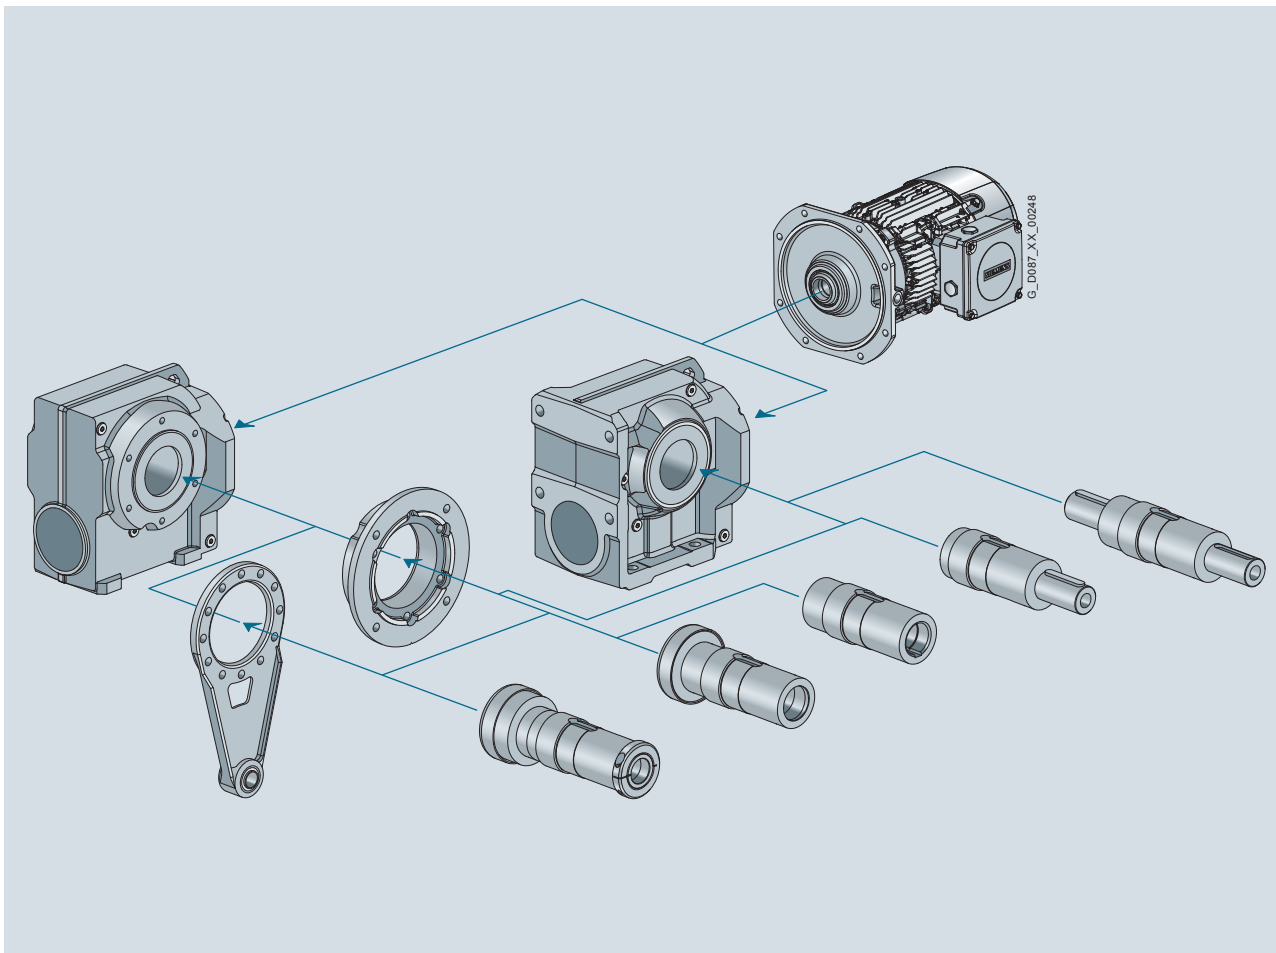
/14 Модуль цилиндрично-червячного редуктора
